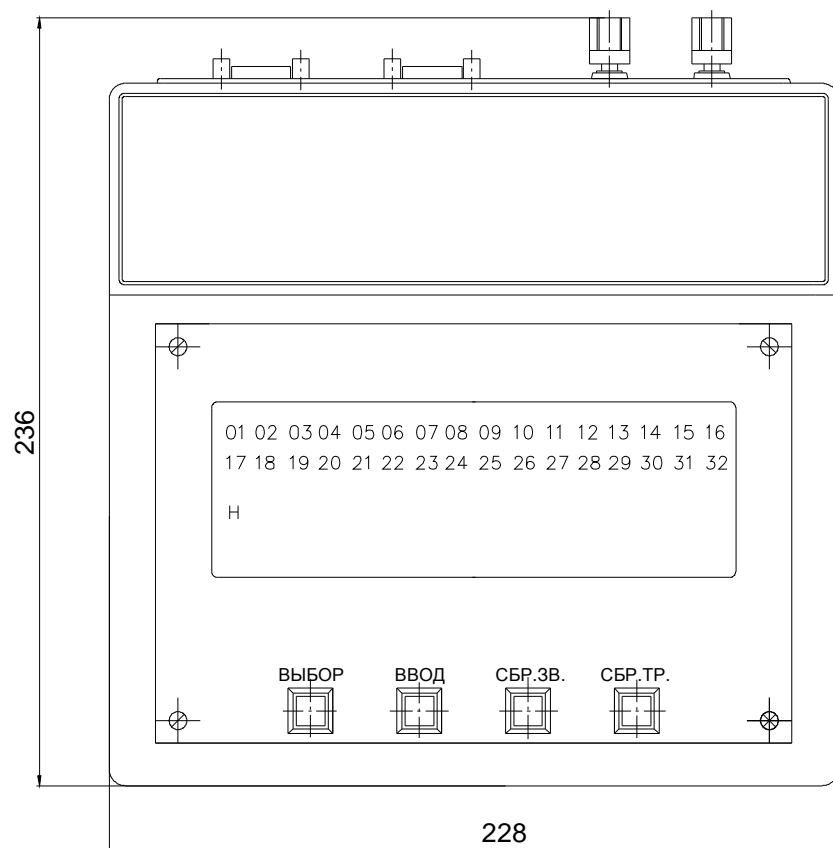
Вид сверху блока обработки РИФ-485 БО
